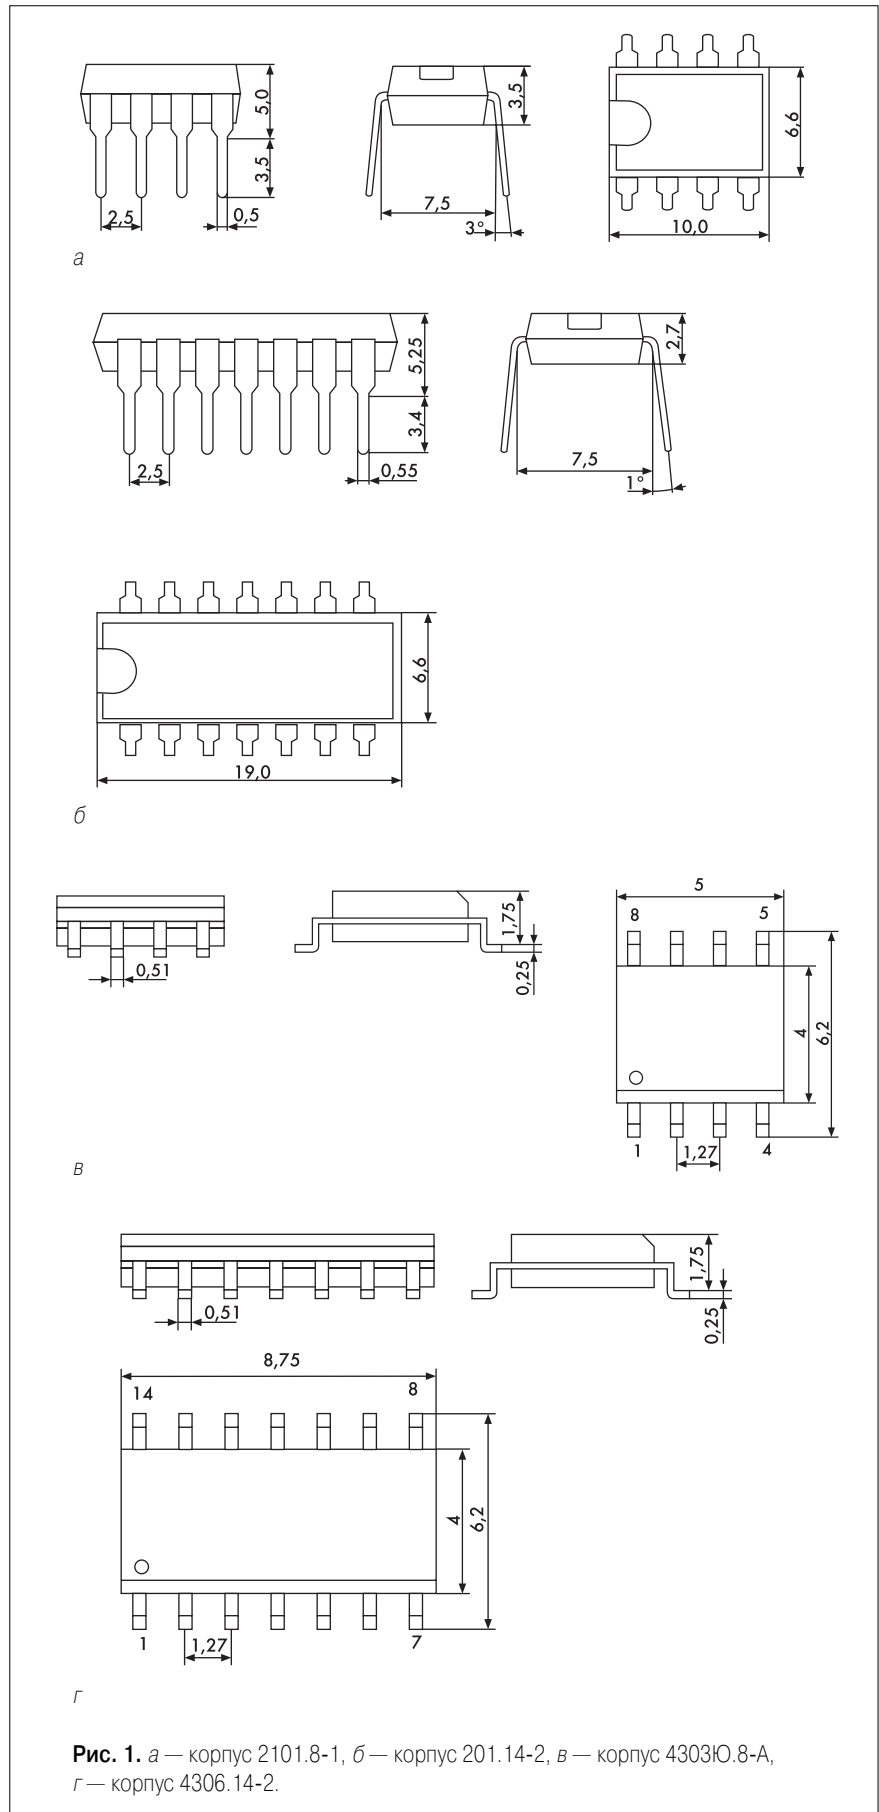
а — корпус 2101.8-1, б — корпус 201.14-2, в — корпус 4303Ю.8-А, г — корпус 4306.14-2.
